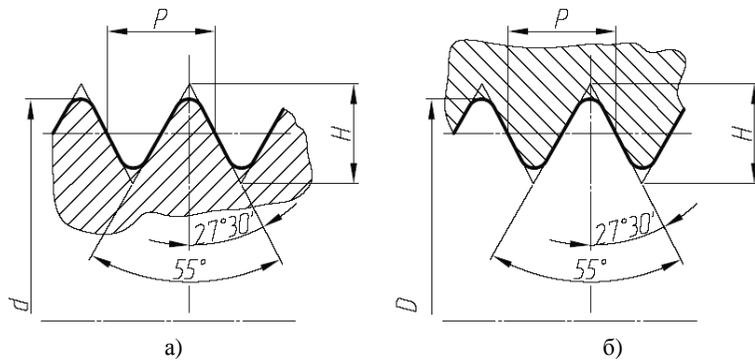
Профиль наружной (а) и внутренней (б) трубной цилиндрической резьбы
